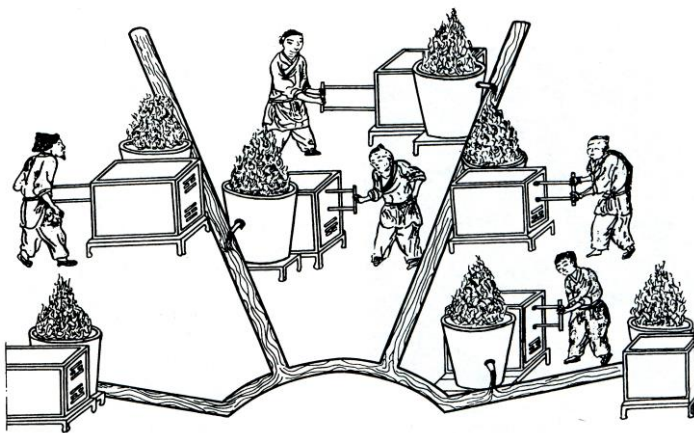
Схема заливки металла из нескольких печей в форму (из старинной китайской книги) [5]
